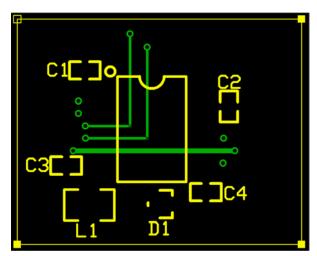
SOIC PCB布局布线(底层金属) (丝网图仅供参考, PCB背面上不存在)
